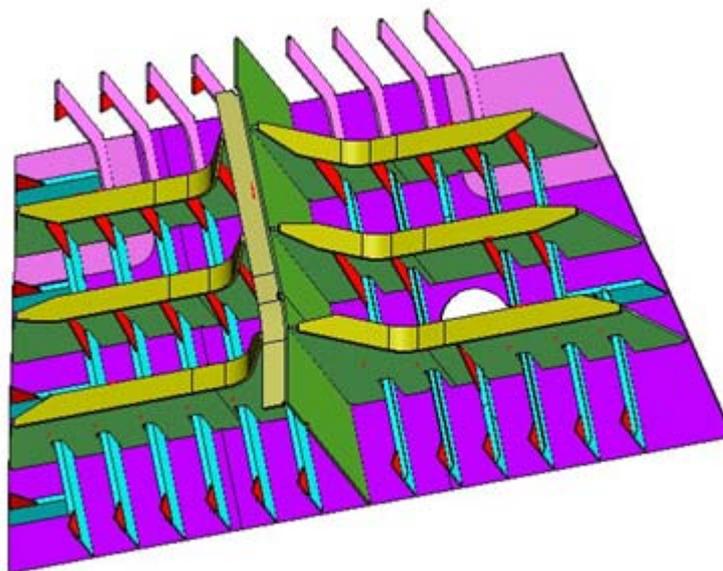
Рамный набор наклонного борта опорного блока МНС
